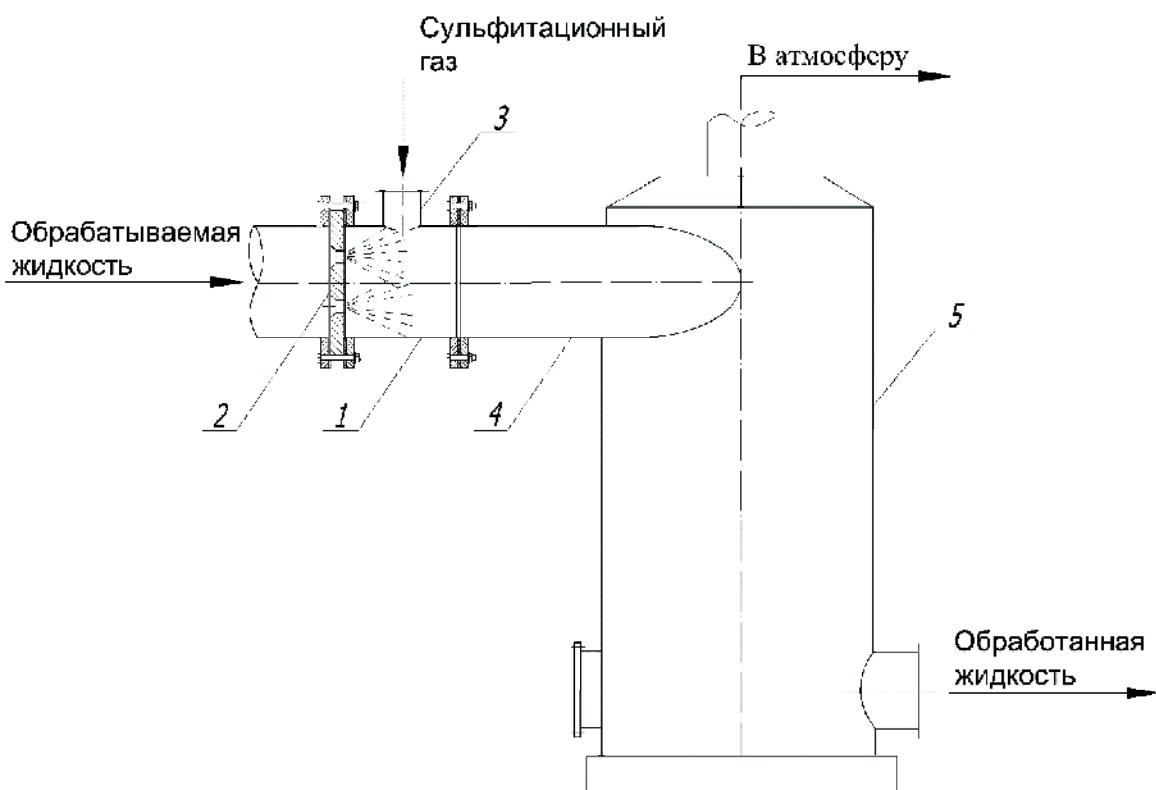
Эскиз сульфитатора жидкостно-струйной конструкции:
